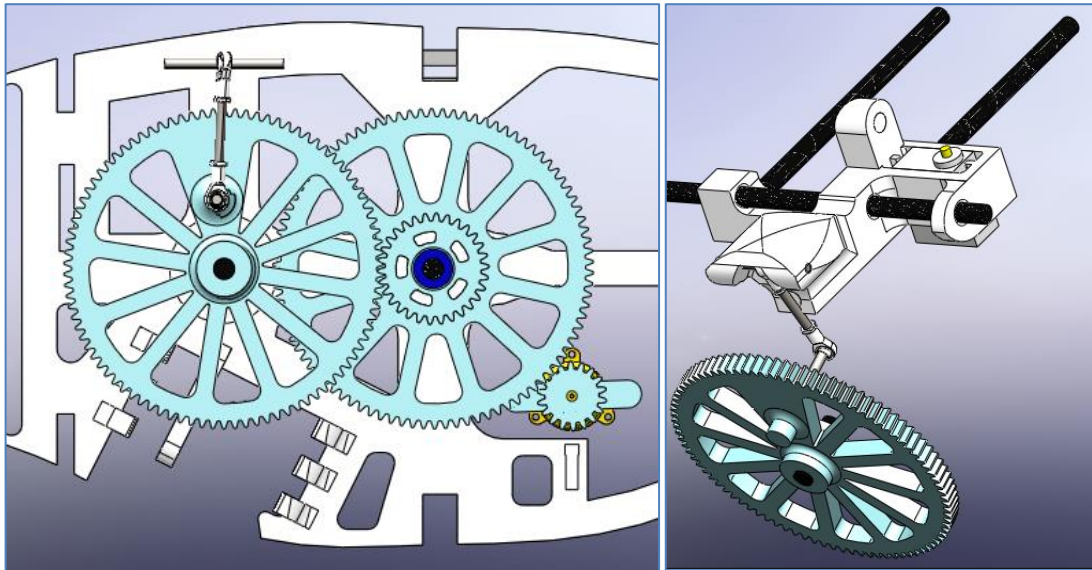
A la izquierda el sistema de engranajes con motor brushless, a la derecha el engranaje unido al hombro del ornitóptero.
